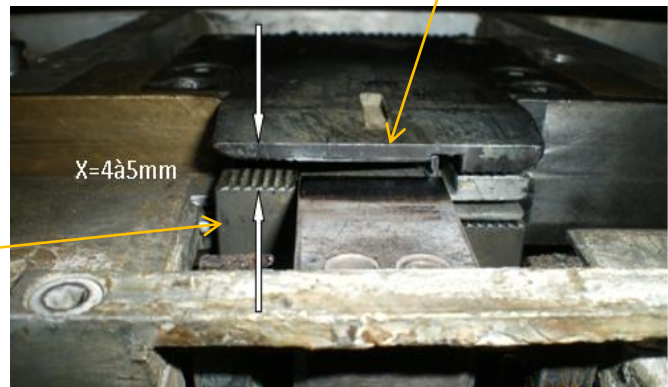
Réglage de jeu entre la Mâchoire et la Plaque
